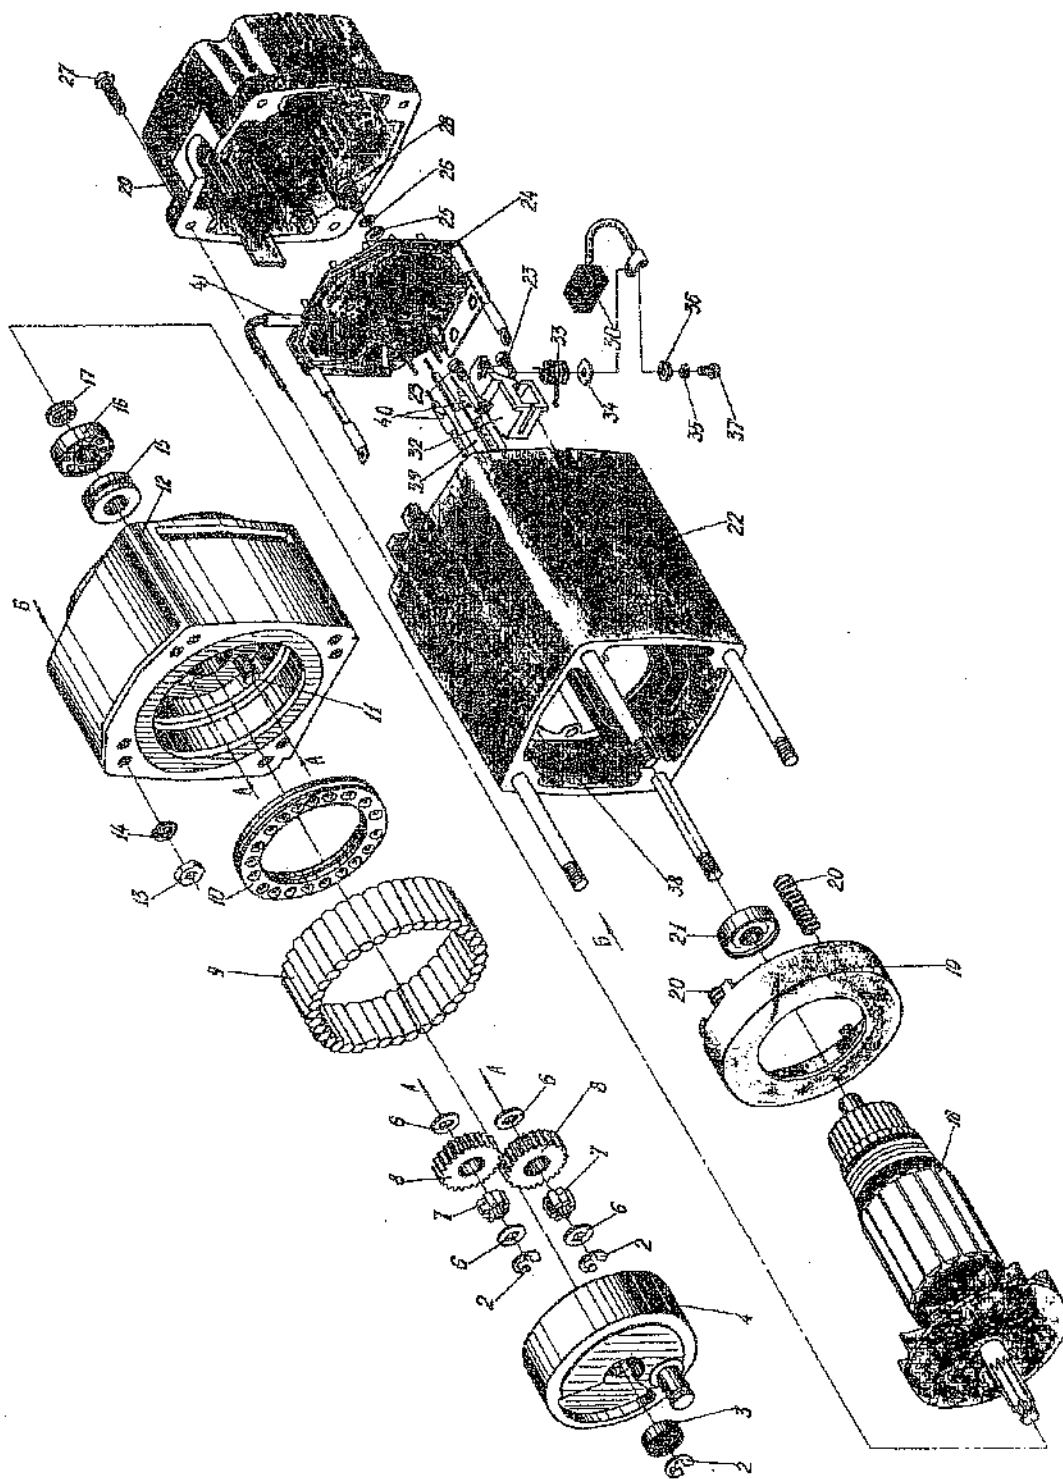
Сборка щита промежуточного с роликовым подшипником и сборка электропривода
